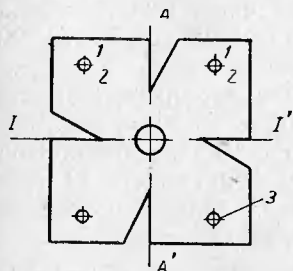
Разметочный шаблон для опорного изолятора с квадратным фланцем.
